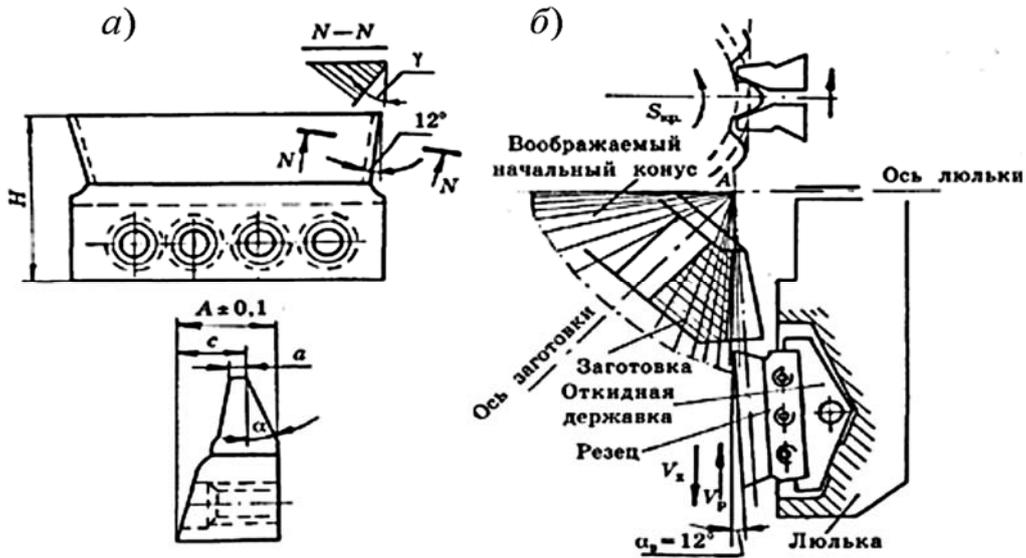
Зубострогальный резец (а) и схема строгания зубьев прямозубых конических колес (б)
